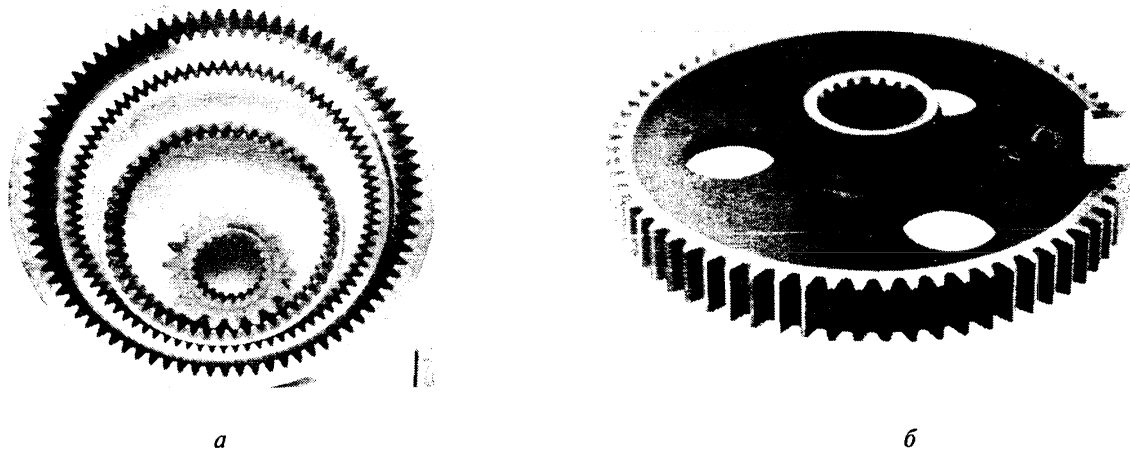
Шестерни, подвергаемые упрочнению индукционной закалкой: а — колесной передачи автомобилей МАЗ, МЗКТ, БелАЗ; б — шестерни конечной передачи трактора "Беларус"
